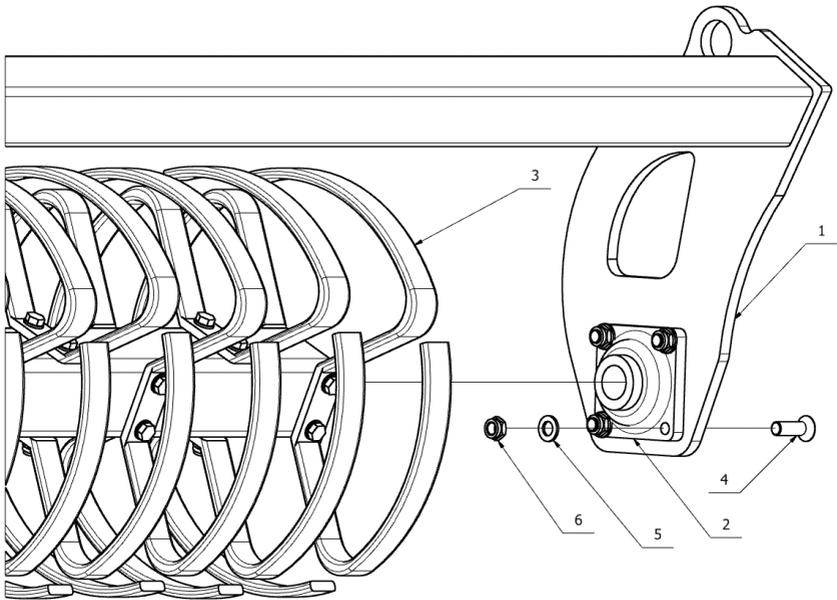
Ø500mm Ringwelle – Lagerbefestigung.
